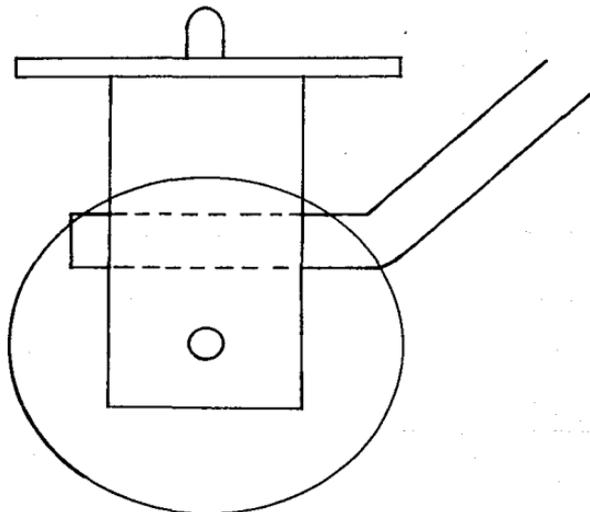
Ensamble del tubo tirador de la grúa.
